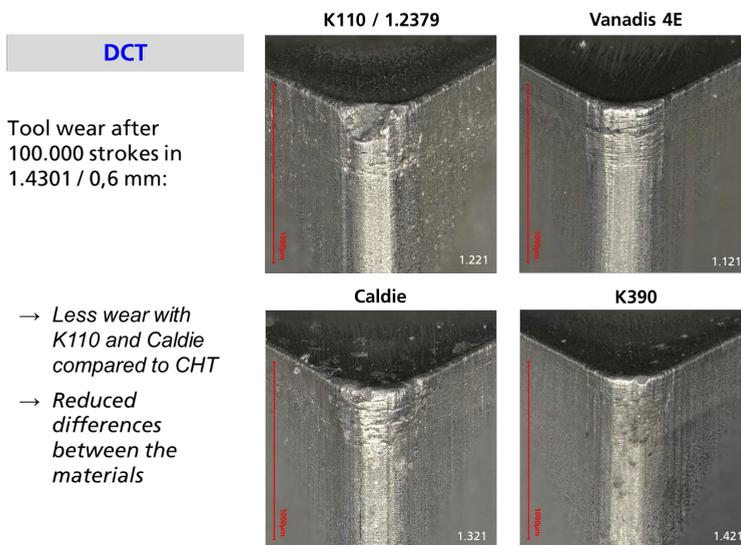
Verschleiß an der Schneidkante von DCT behandelten Schneidwerkzeugen abhängig vom Werkzeugwerkstoff
